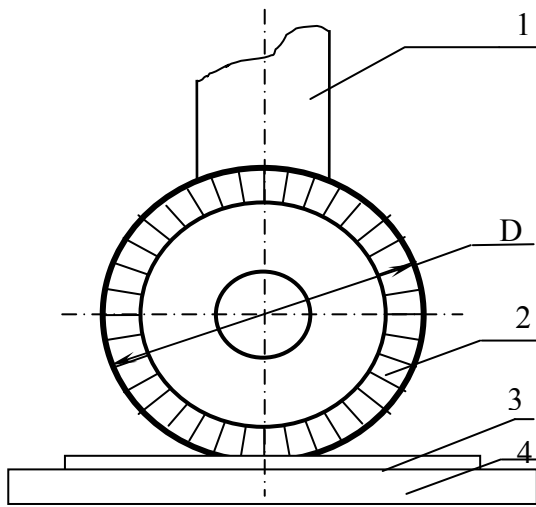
Схема для определения коэффициента резания  $f$ : 1 - электрошлифмашина; 2 - полимерно-абразивная щетка; 3 - обрабатываемая пластина; 4 - стол фрезерного станка; D - диаметр щетки.
